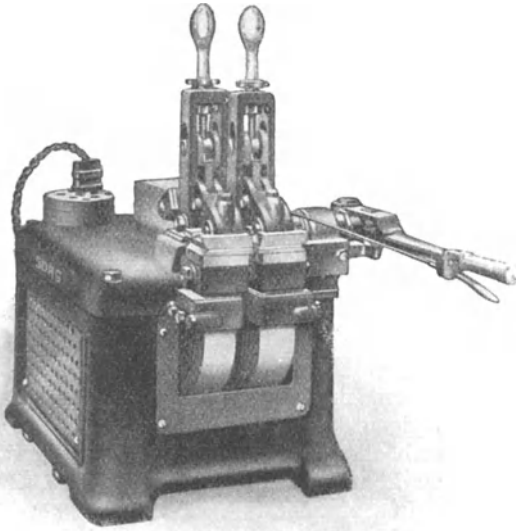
Kleine Stumpfschweißmaschine mit Schnelleinspannvorrichtung.
